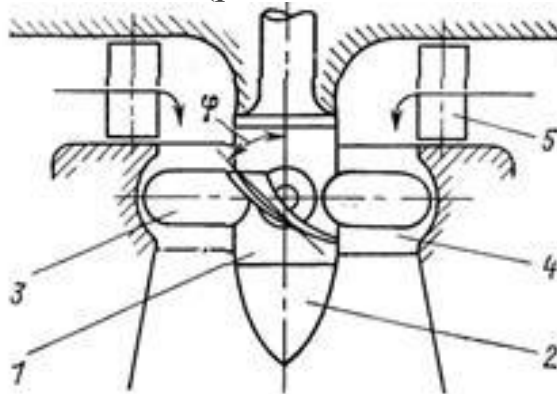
Рабочее колесо поворотно-лопастной турбины: 1 — корпус рабочего колеса; 2 — обтекатель; 3 — лопасти; 4 — камера рабочего колеса; 5 — лопатки направляющего аппарата.
